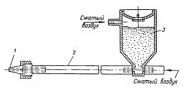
2. Нагнетательный дробеструйный аппарат: 1 — сопло; 2 — шланг; 3 — абразивный матернал
